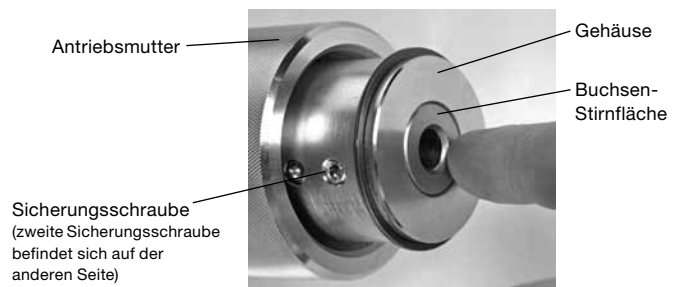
Anbringen der Anfaswerkzeugbuchse
